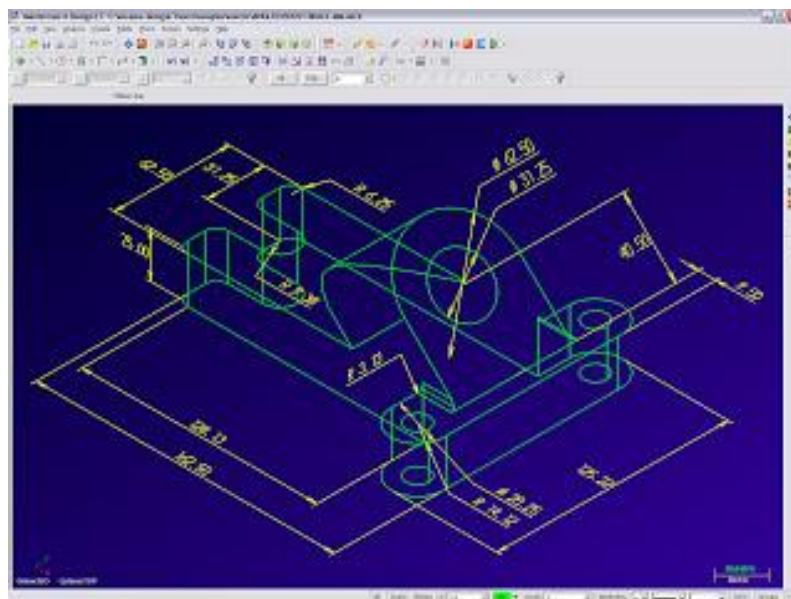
Ferramenta de CAD do Mastecam [31].
